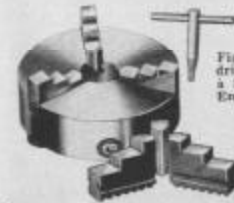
Mandrin Universel à 3 Mors avec Engrenage en Spirale
